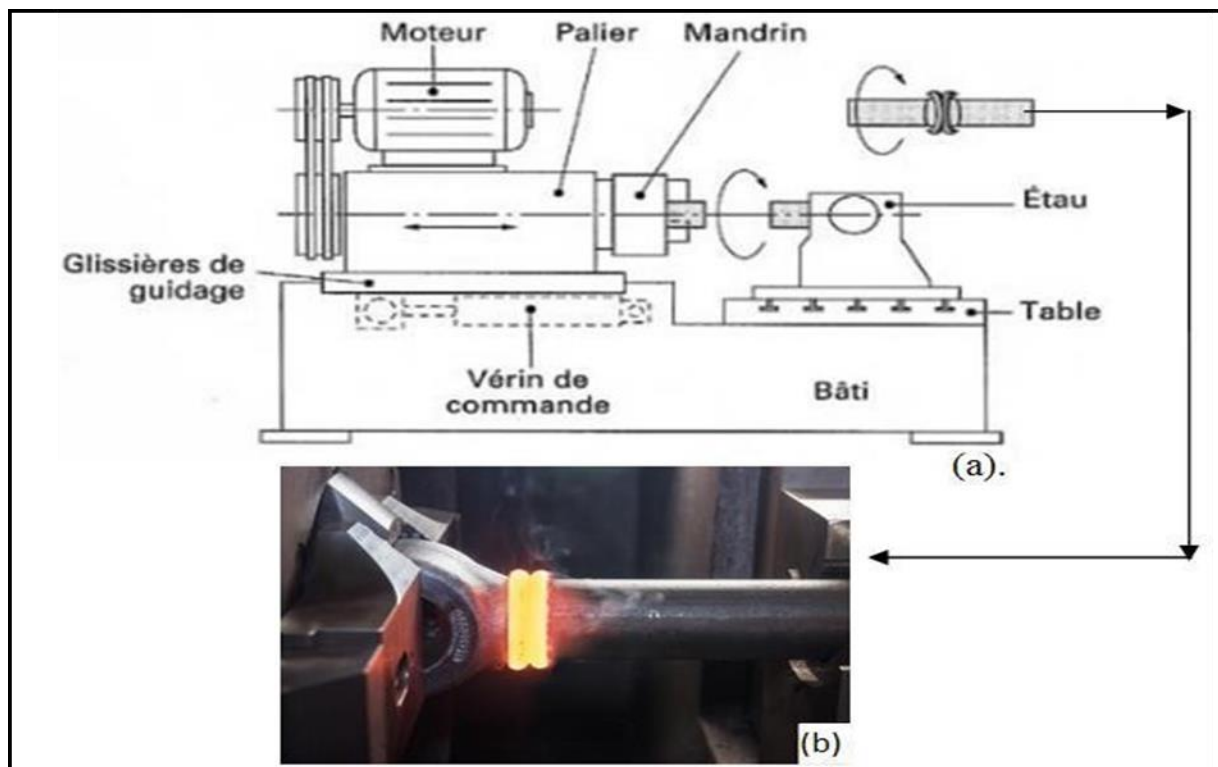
Soudage par friction (a) : schéma d'une machine de soudage par friction
